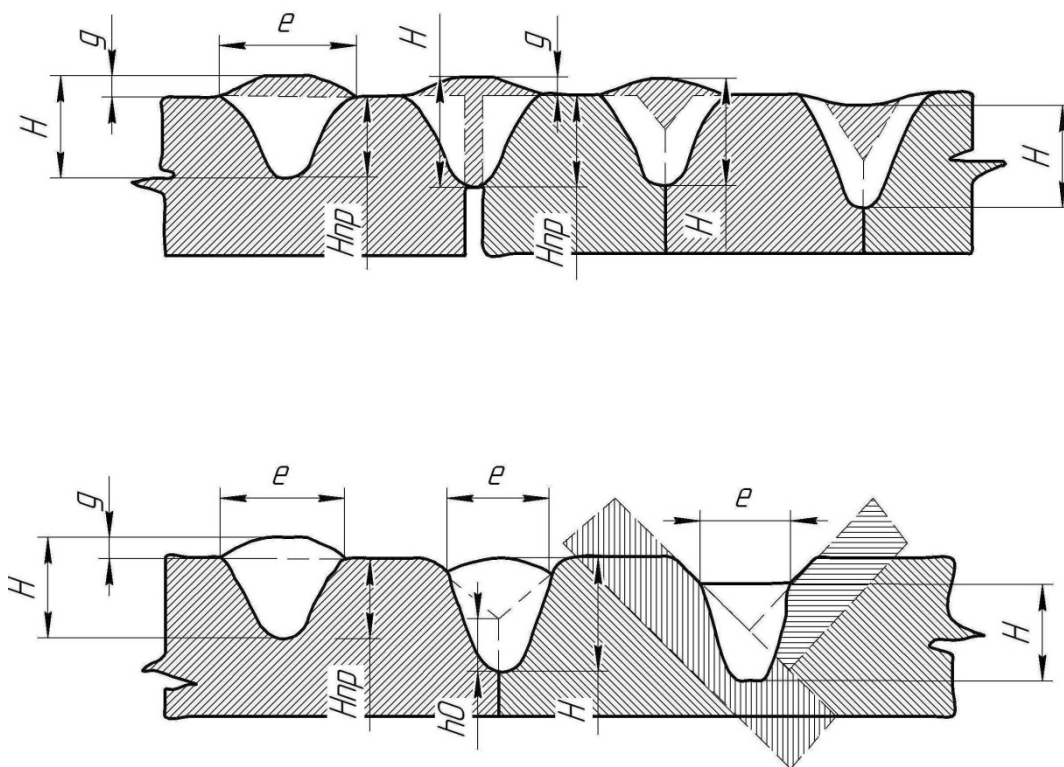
Влияние типа шва, зазоров и разделки на профиль провара между основными размерами шва
